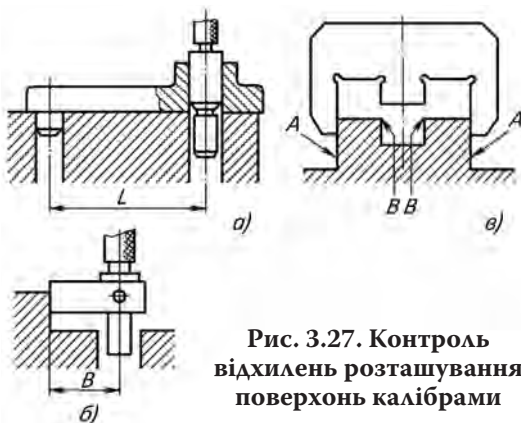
Контроль відхилень розташування поверхнь калібрами
